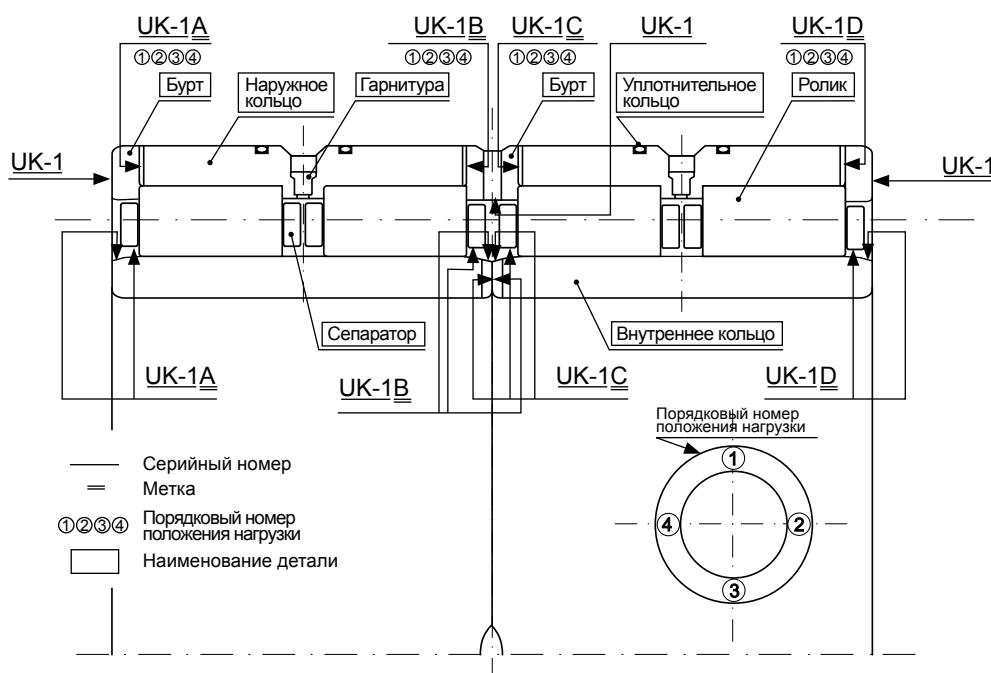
Наименования и примеры маркировки деталей (четырёхрядный цилиндрический роликоподшипник).
